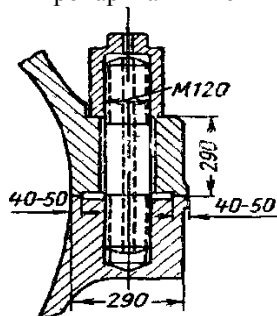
Приспособление для передвижения крышки цилиндра при шабровке фланцев разъема.
